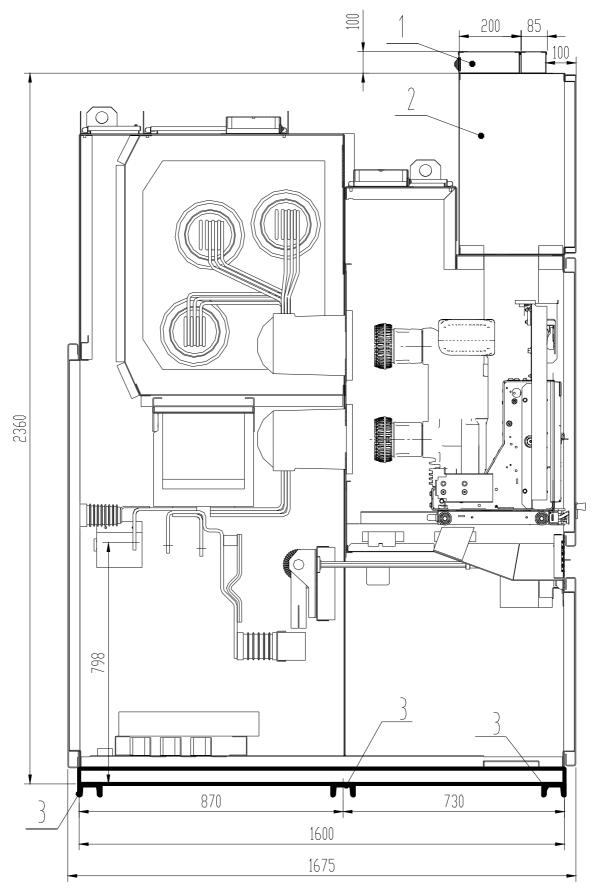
Габаритные и установочные размеры К-БЭМН
